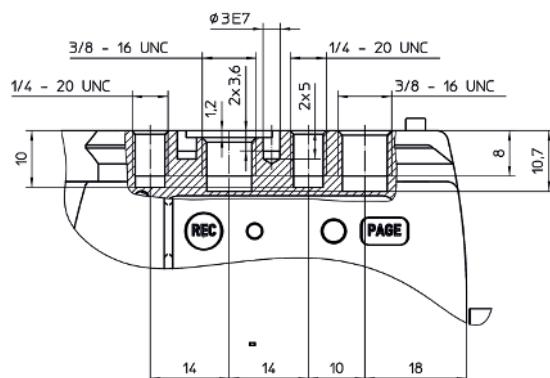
Hi-5 : dettaglio vista frontale X
